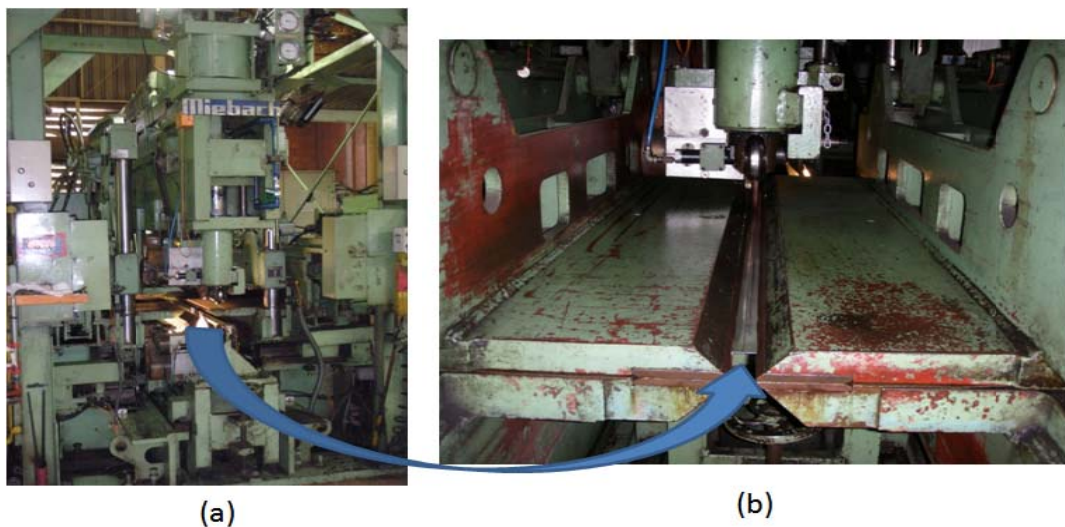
(a) vista lateral da Máquina de Solda por costura e (b) vista superior da tira em processo de soldagem.
